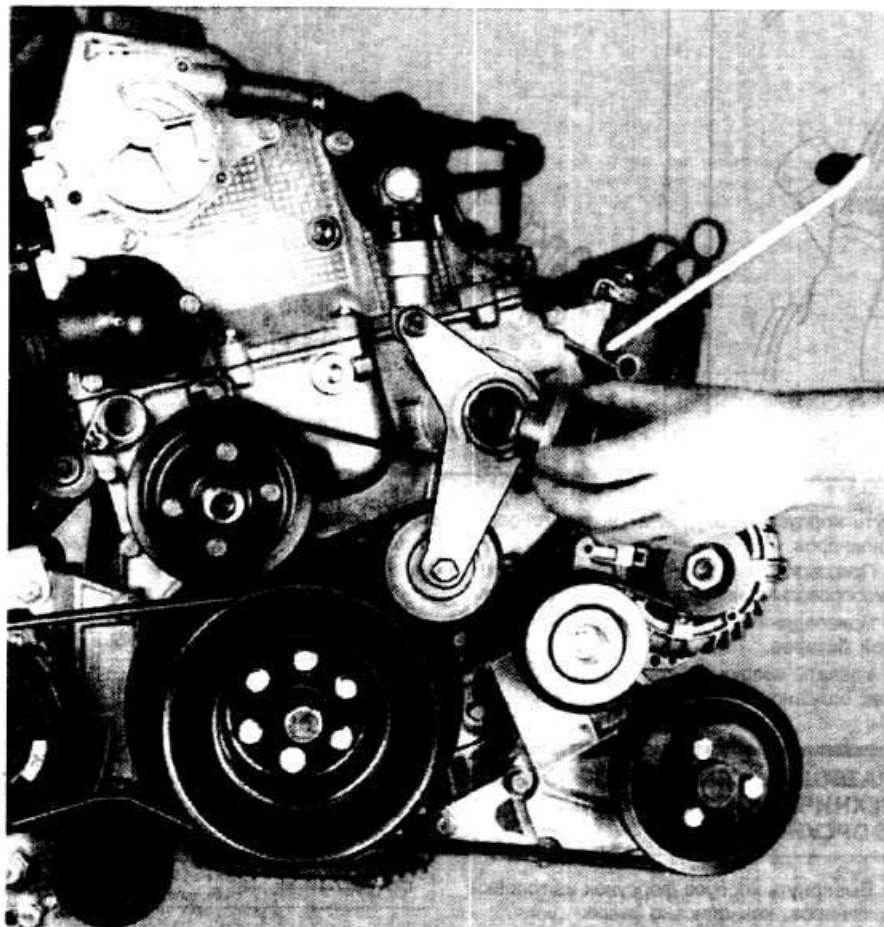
Снятие заглушки натяжителя ремня привода вспомогательных агрегатов
